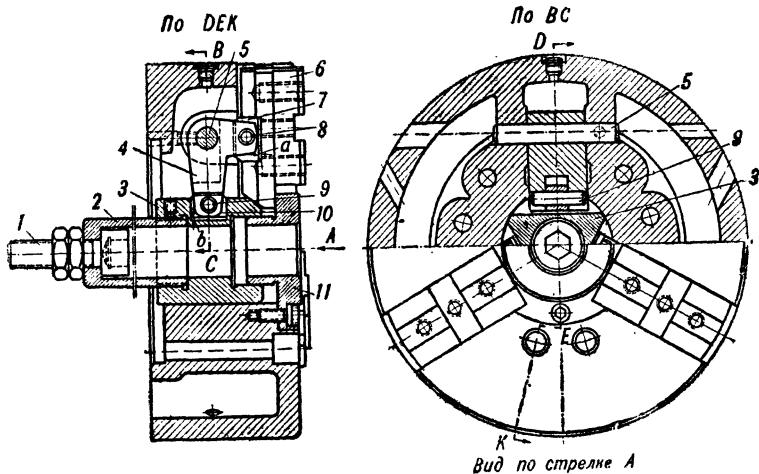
Трехкулачковый пневматический самоцентрирующий патрон с коленчато-рычажным механизмом.
